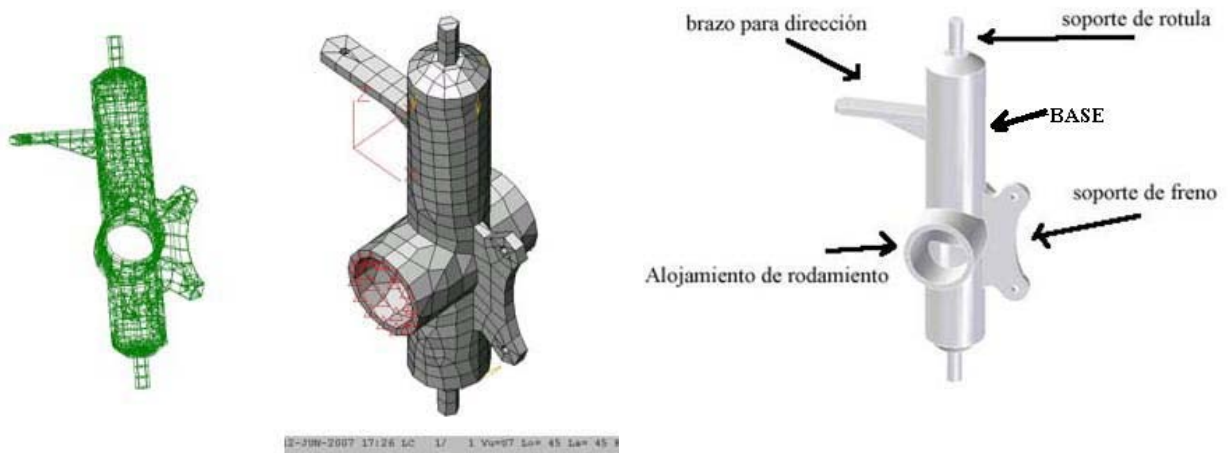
Pieza optimizada y modelada en CAD, para su manufactura.
